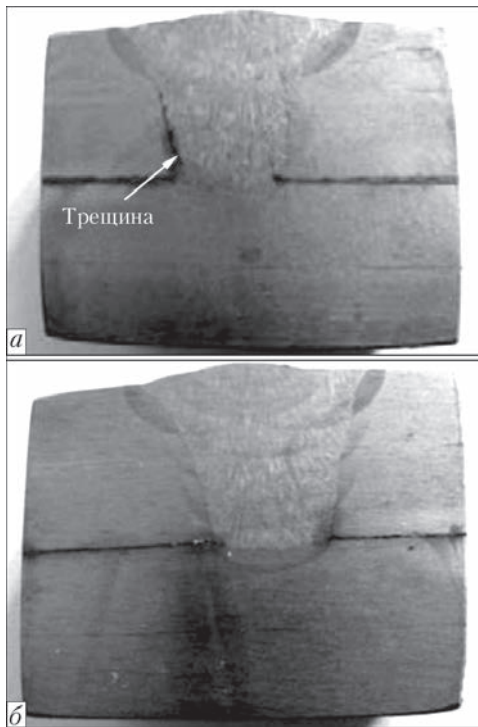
Шлифы пробы «Marine» при механизированной сварке: а — без предварительного подогрева; б — с предварительным и сопутствующим подогревом до 160...180 °С
